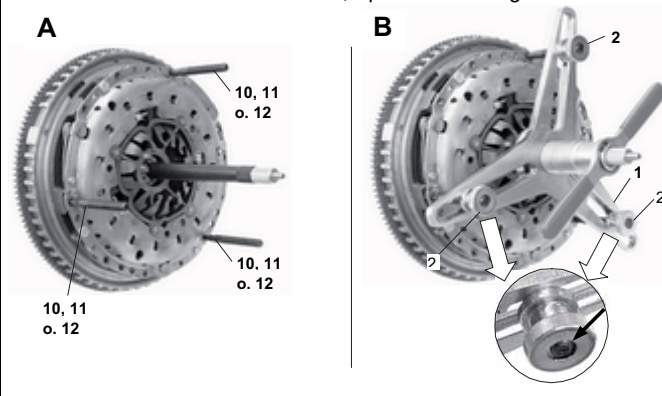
Druckspindel eindrehen, Befestigungsschrauben einschrauben.
